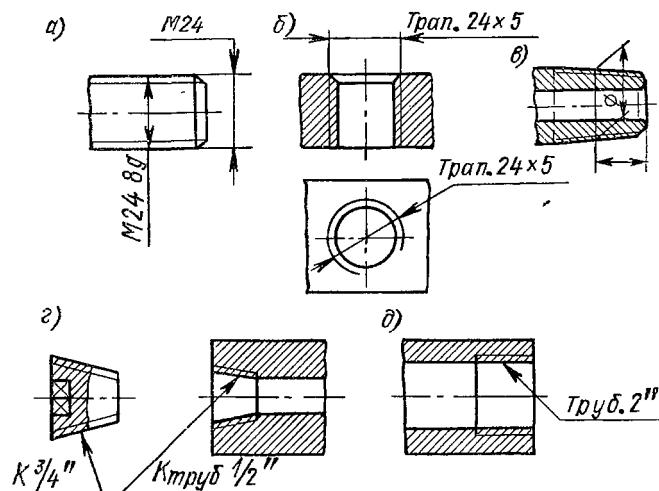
Примеры обозначения резьбы на чертежах: а — метрическая резьба; б — трапецидальная резьба; в — нанесение размеров конической резьбы при заданных расположении и диаметре основной плоскости резьбы; г — коническая резьба; д — цилиндрическая трубная резьба
